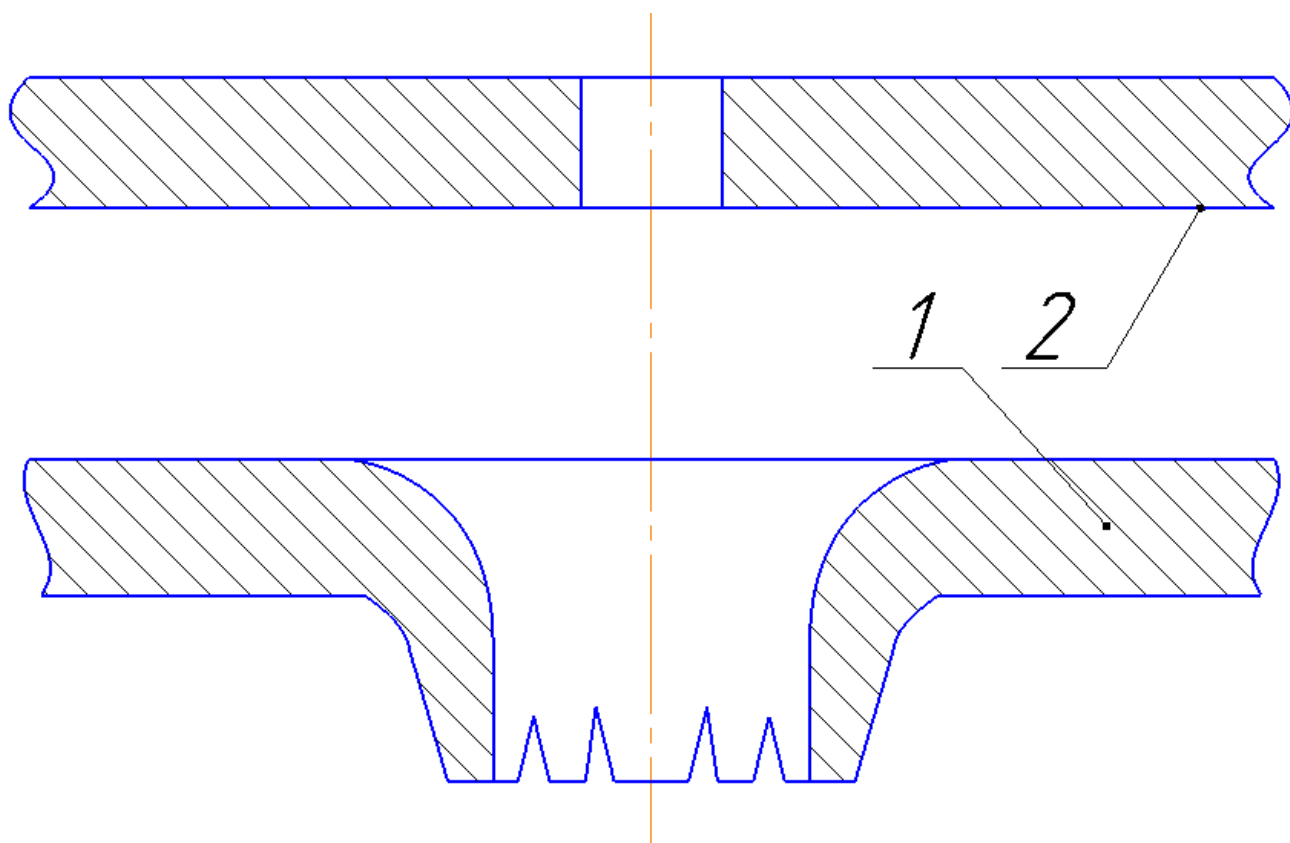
Получение отверстия с отбортовкой с использованием предварительной пробивки [9]: 1 – заготовка с предварительно пробитым отверстием; 2 – заготовка с отверстием с отбортовкой
